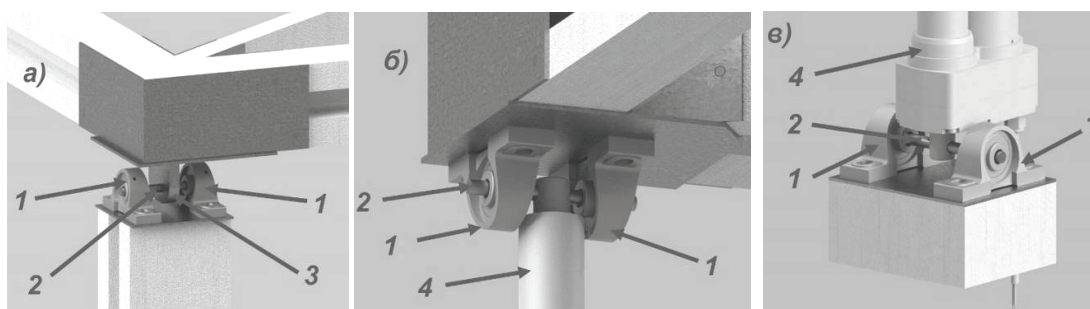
а) Узел 1; б) Узел 2; в) Узел 3; 1 – подшипник самовыравнивающийся на опоре; 2 – оси (втулки); 3 – проушина; 4 – линейный актуатор (электроцилиндр)
